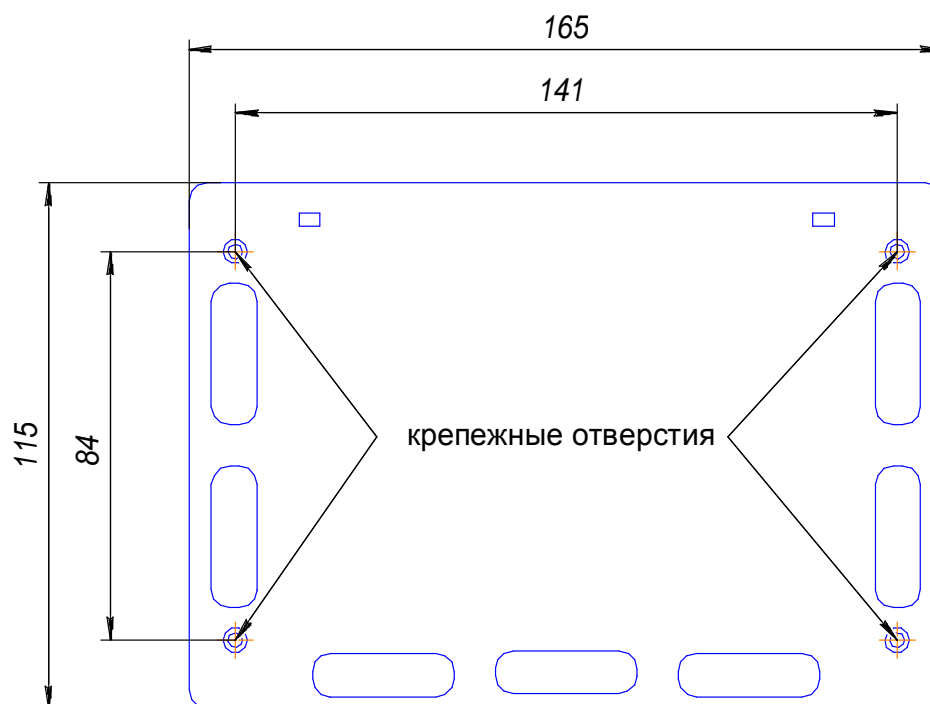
а. Разметка крепления АКШ ФИДШ.426461.001 в пластмассовом корпусе
